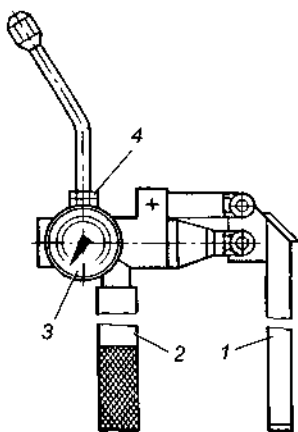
Устройство КИ-16301А для проверки форсунок и прецизионных пар топливного насоса: 1 — приводная ручка; 2 — ручка-резервуар; 3 — манометр; 4 — переходник
